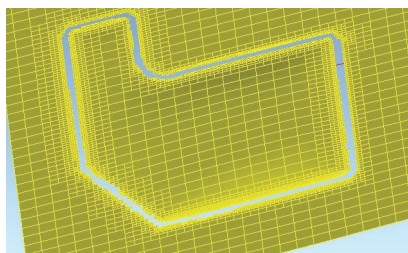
Полученный контур заготовки для детали типа «уголок»
